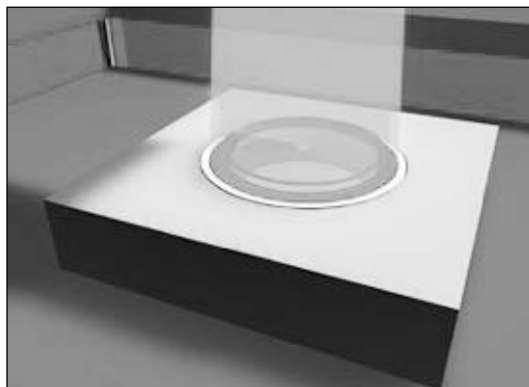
Сварка кольцевым лазерным лучом
